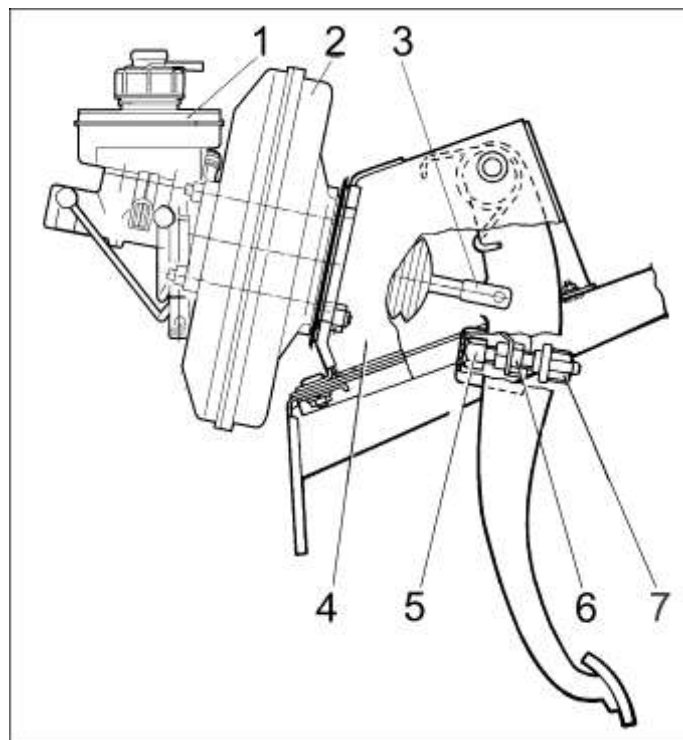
а. Вакуумный усилитель тормозов 2123-3510006-11 с главным цилиндром и бачком в сборе (устанавливается на автомобилях с 09.2005 г. выпуска):
